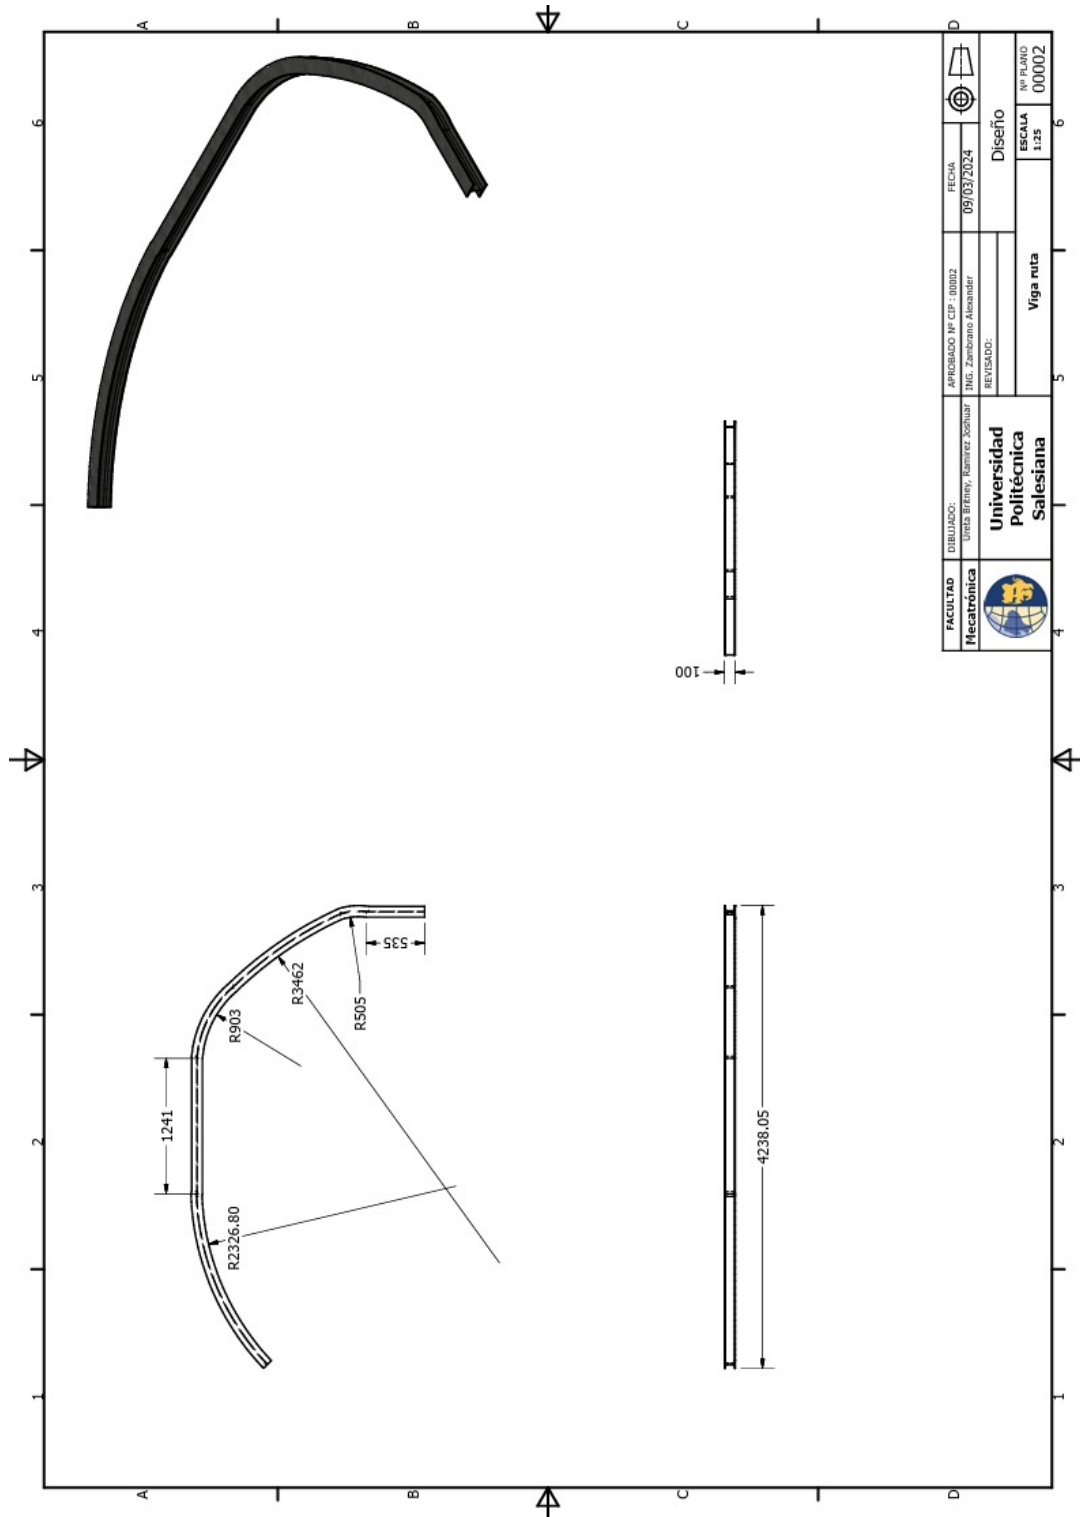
Viga ruta, Fuente: J.Ramirez, B.Ureta
